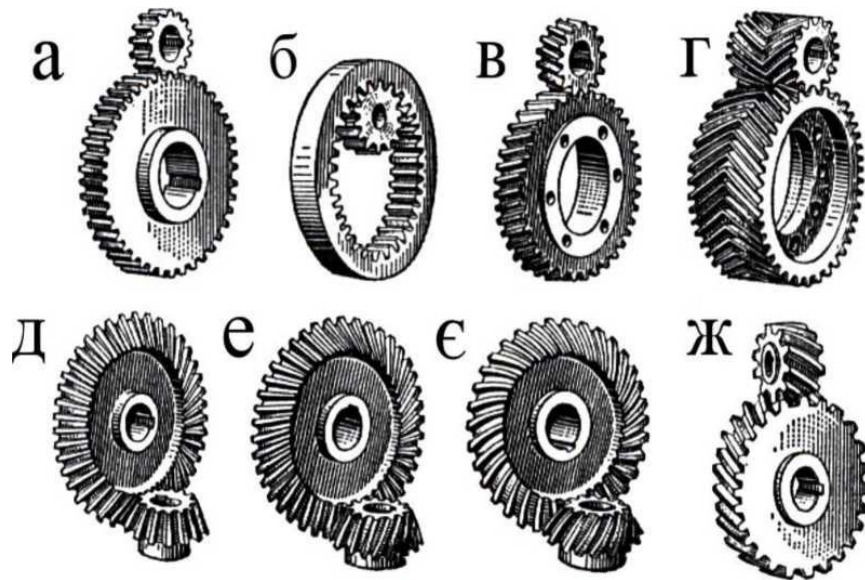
Види зубчастих передач: а, б, в, г - циліндричні передачі при паралельних валах; д, е, є, ж - конічні, осі яких перетинаються; а, б - зубчасті передачі з зовнішнім зачепленням та внутрішнім відповідно; а, б, д - прямозубі передачі; в, е - косо зубі; г - шевронні; ж - кругові.
